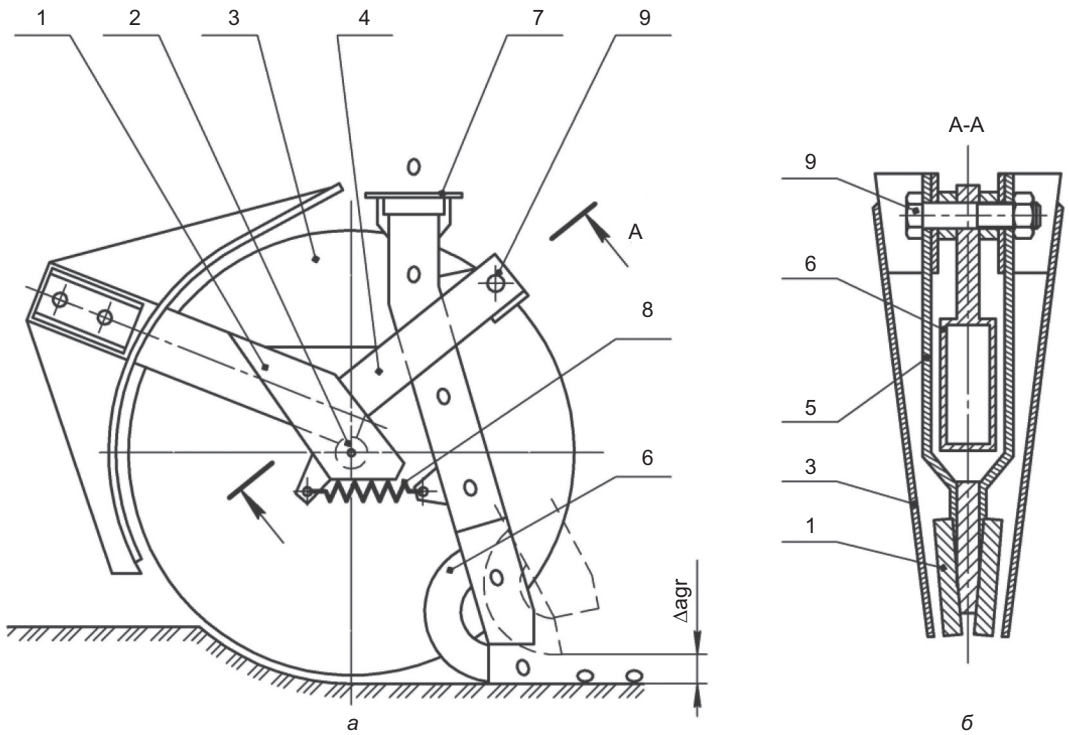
Схема комбінованого дводисково-анкерного сошника: а — вид збоку при знятому лівому диску; б — перетин по А-А: 1 — корпус; 2 — вісь; 3 — диск; 4 — тримач; 5 — щока; 6 — розтруб; 7 — наральник; 8 — пружина; 9 — шарнірна підвіска
